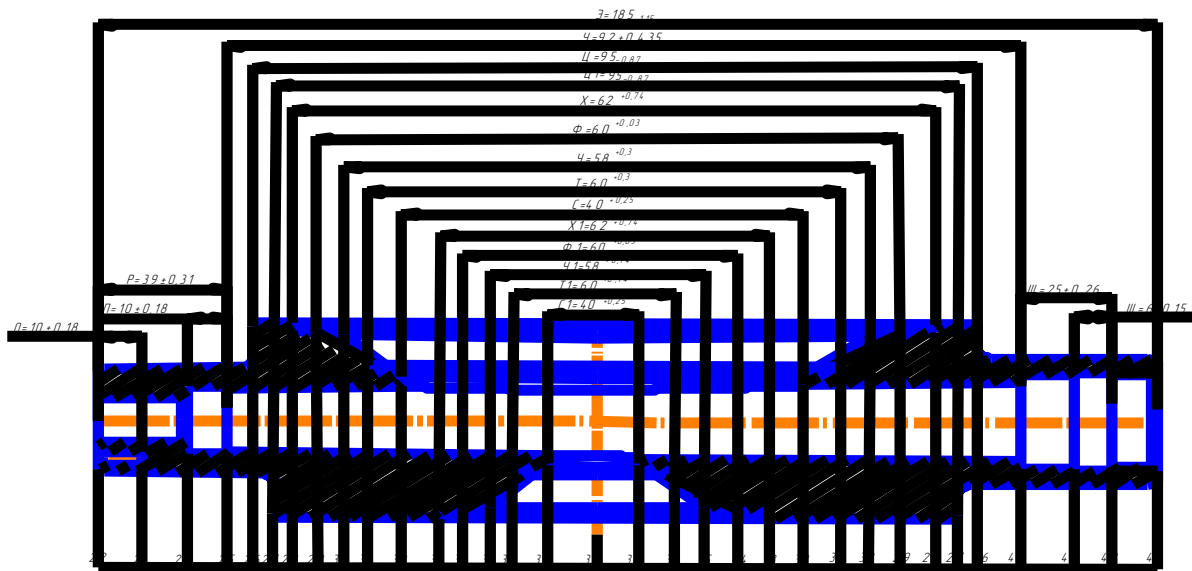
Преобразованный чертеж детали во II проекции
